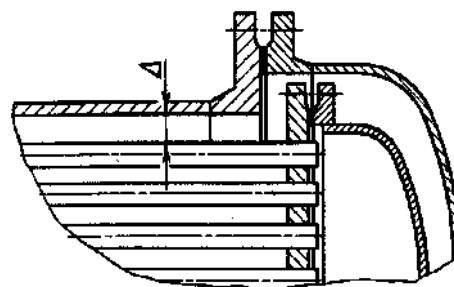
Вариант размещения крышки плавающей головки в кожухе меньшего диаметра
